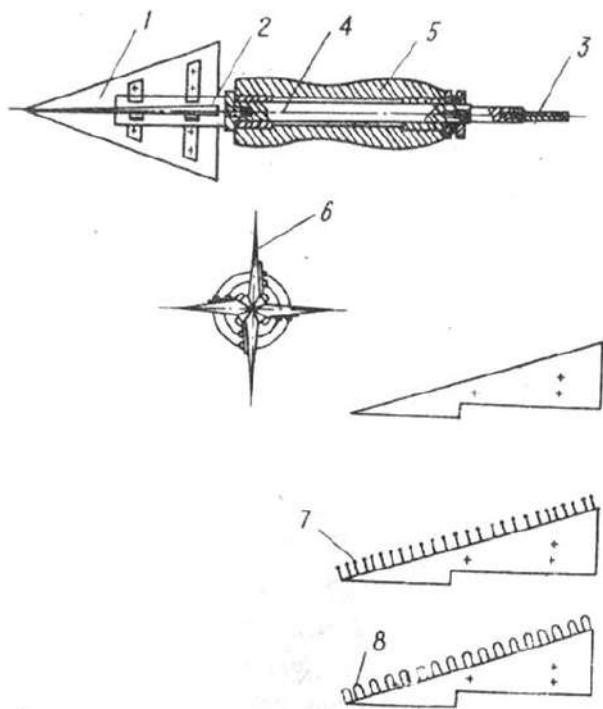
Устройство для сбора ягод: 1 – шпindelь; 2 – вал; 3 – гибкий валик; 4 – промежуточное звено; 5 – рукоятка; 6 – радиальные ребра; 7 – утолщения на концах; 8 – петля
